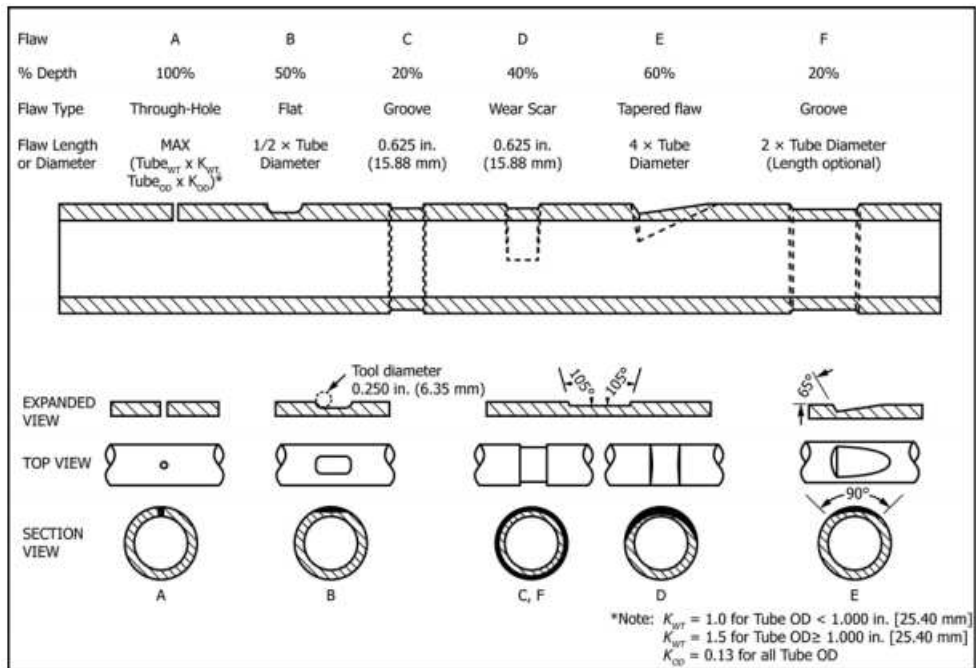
Desenho técnico de um tubo padrão para calibração do sistema RFT (Fonte: ASTM, 2019).
